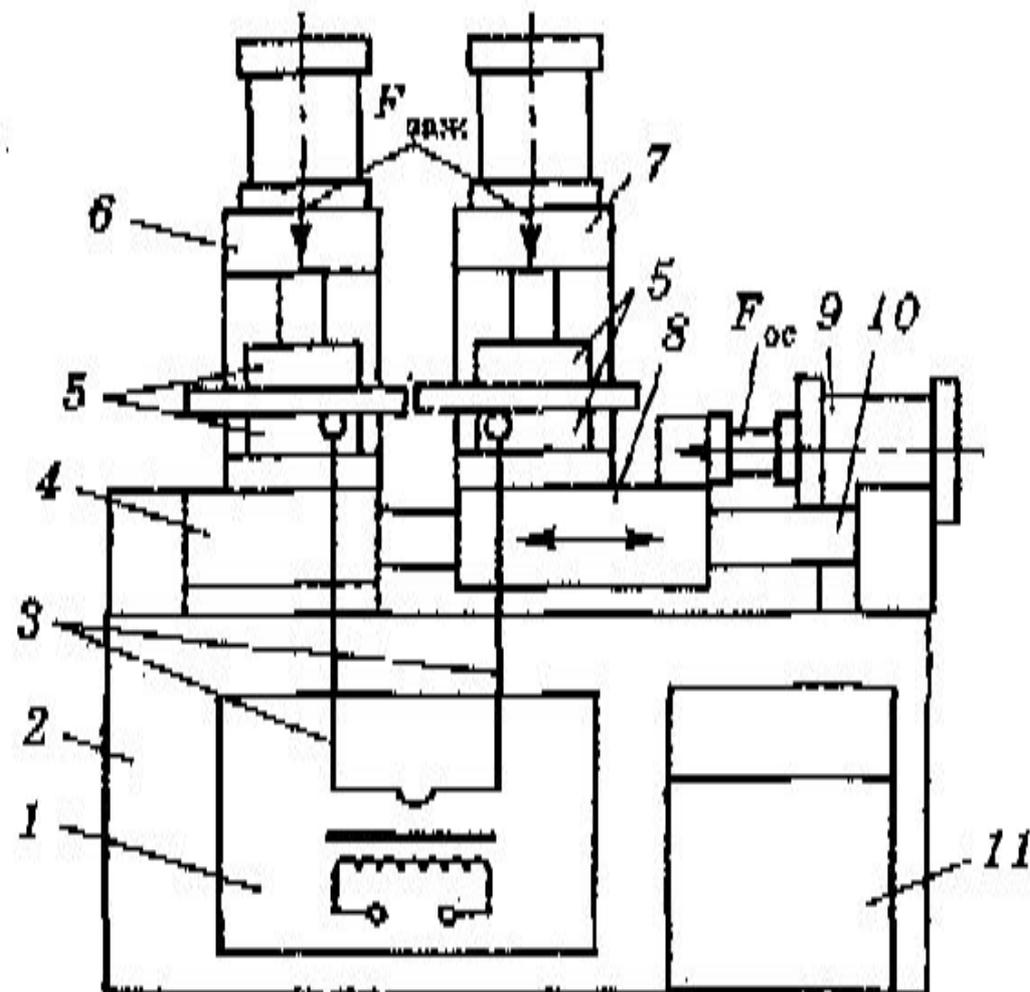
Конструктивная схема машины для стыковой сварки
